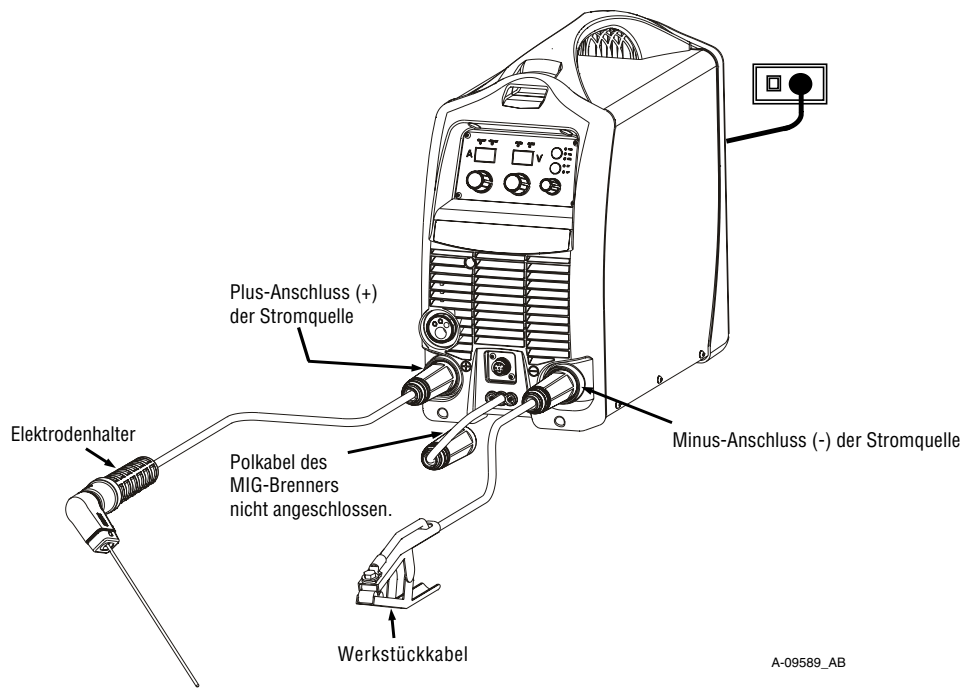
Konfiguration für Manuelles Lichtbogenschweißen
